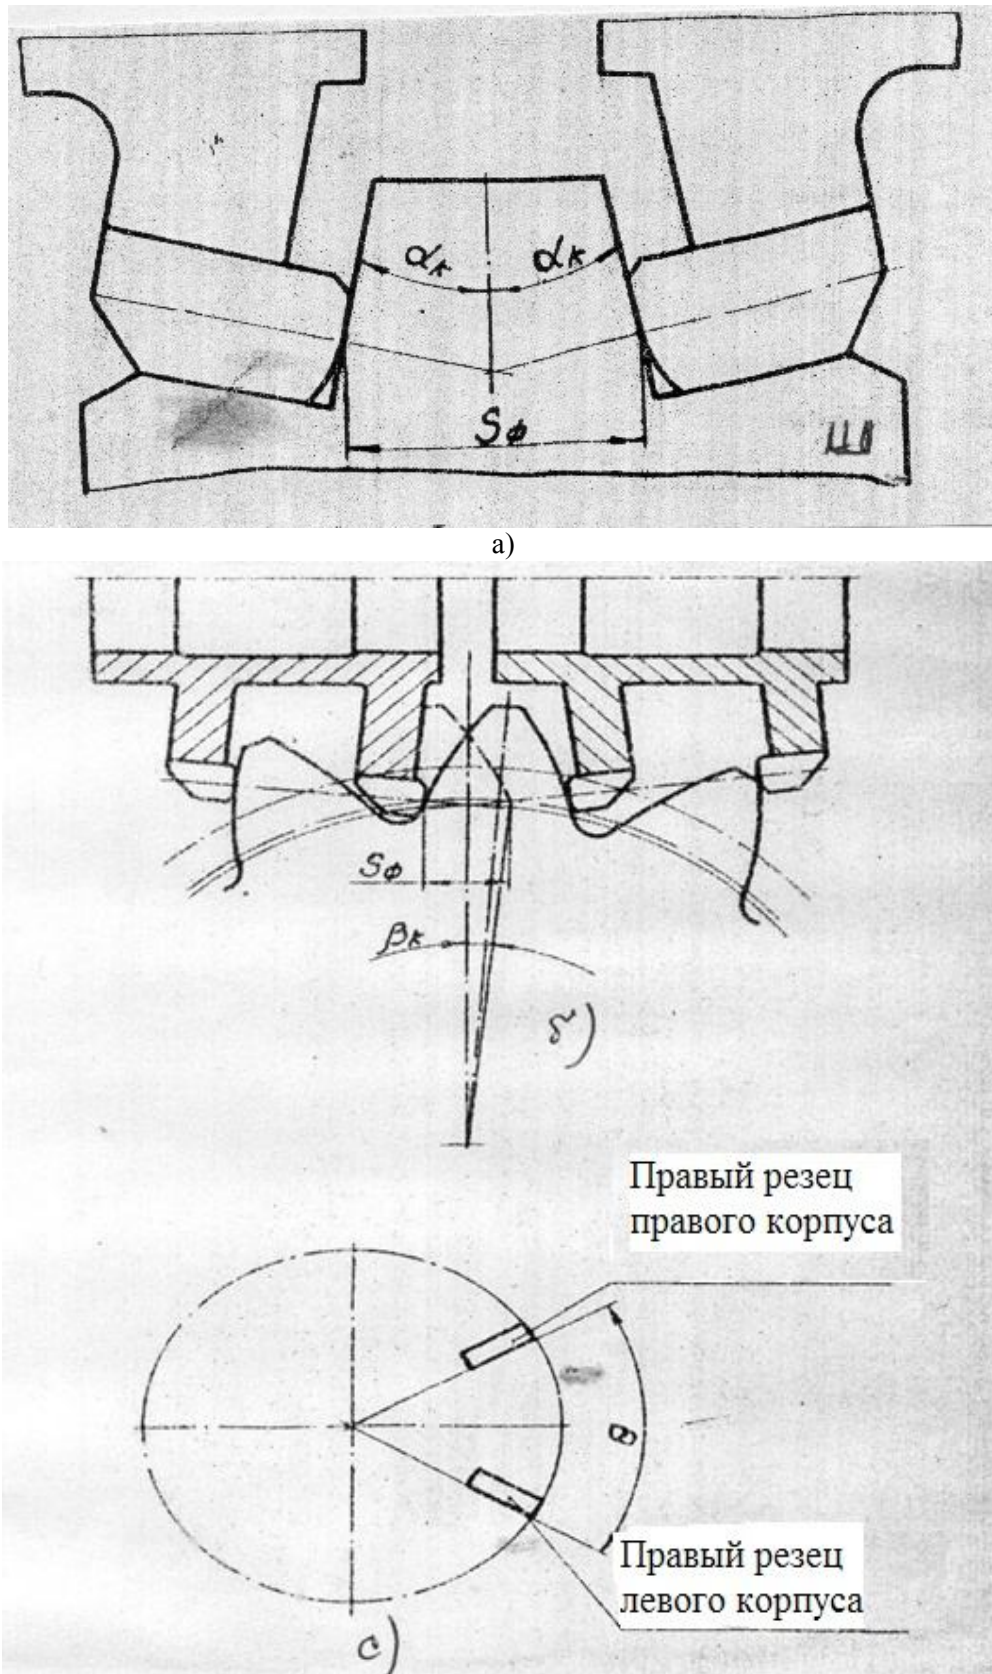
К установке и настройке фрезы. а - шаблон для установки корпусов; б - поворот колеса на угол  $\beta_k$ ; в - разворот корпусов фрезы на угол  $\theta$ .
